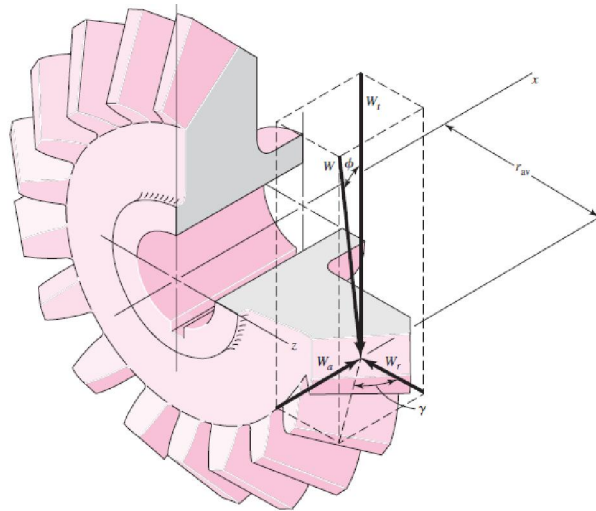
Fuerzas que actúan en los dientes de un engrane cónico
